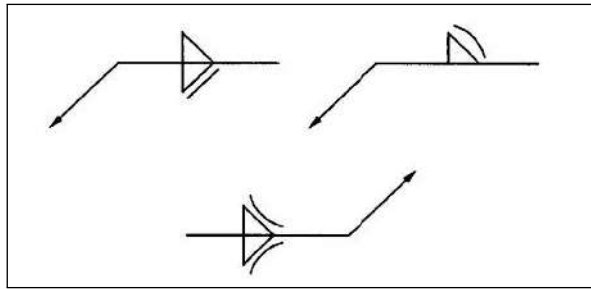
Aplicación de símbolos, Contorno o cabado de soldadura obtenido por el mismo proceso de soldar
